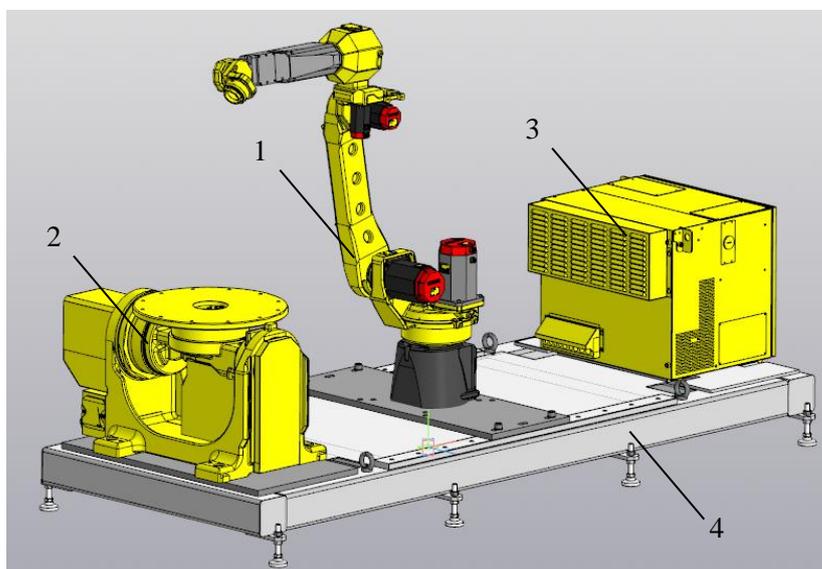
Роботизированная сварочная ячейка
